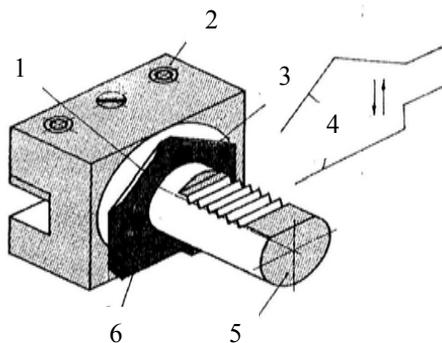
Вариант конструктивного исполнения автоматически сменяемой резцовой державки:
